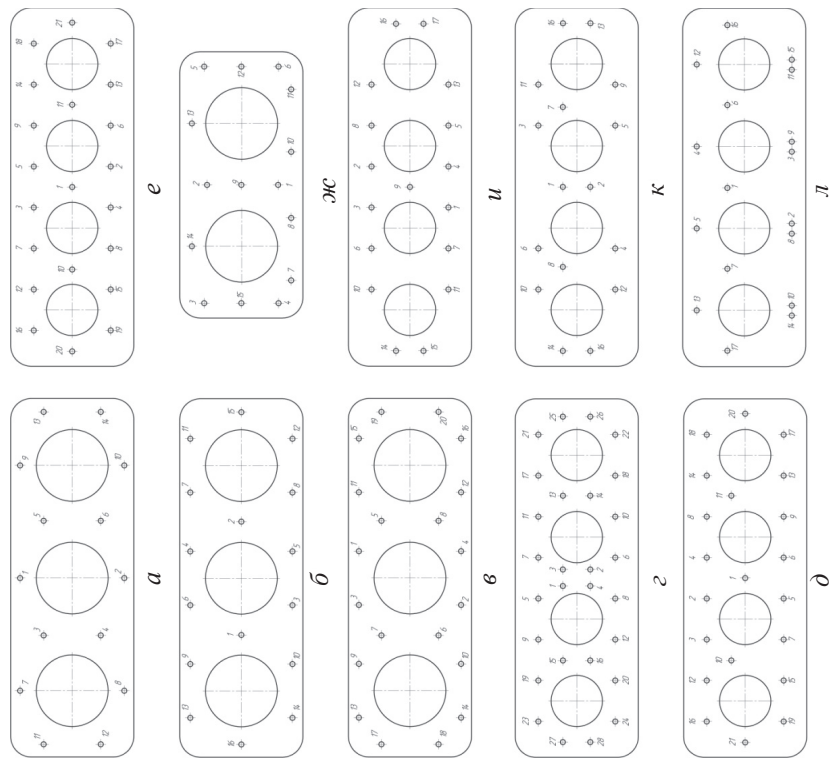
Последовательность затяжки гаек крепления головок цилиндров двигателей: а – ЯМЗ-240Б; б – СМД-60, СМД-62 и СМД-64; в – А-01М; г – Д-48Л, Д-48М, Д-65М и Д-65Н; е – ЯМЗ-238НБ; ж – Д-108; з – СМД-14 и его модификации; к – Д-240, Д-240Л; л – ЗИЛ-130
